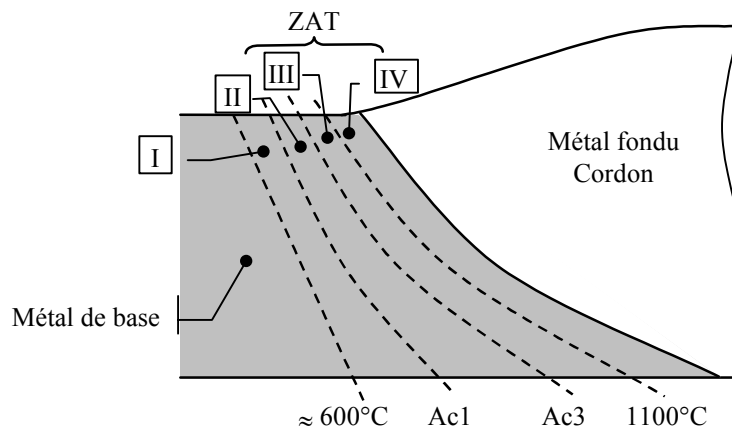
Zone affectée thermiquement d'un cordon de soudure
